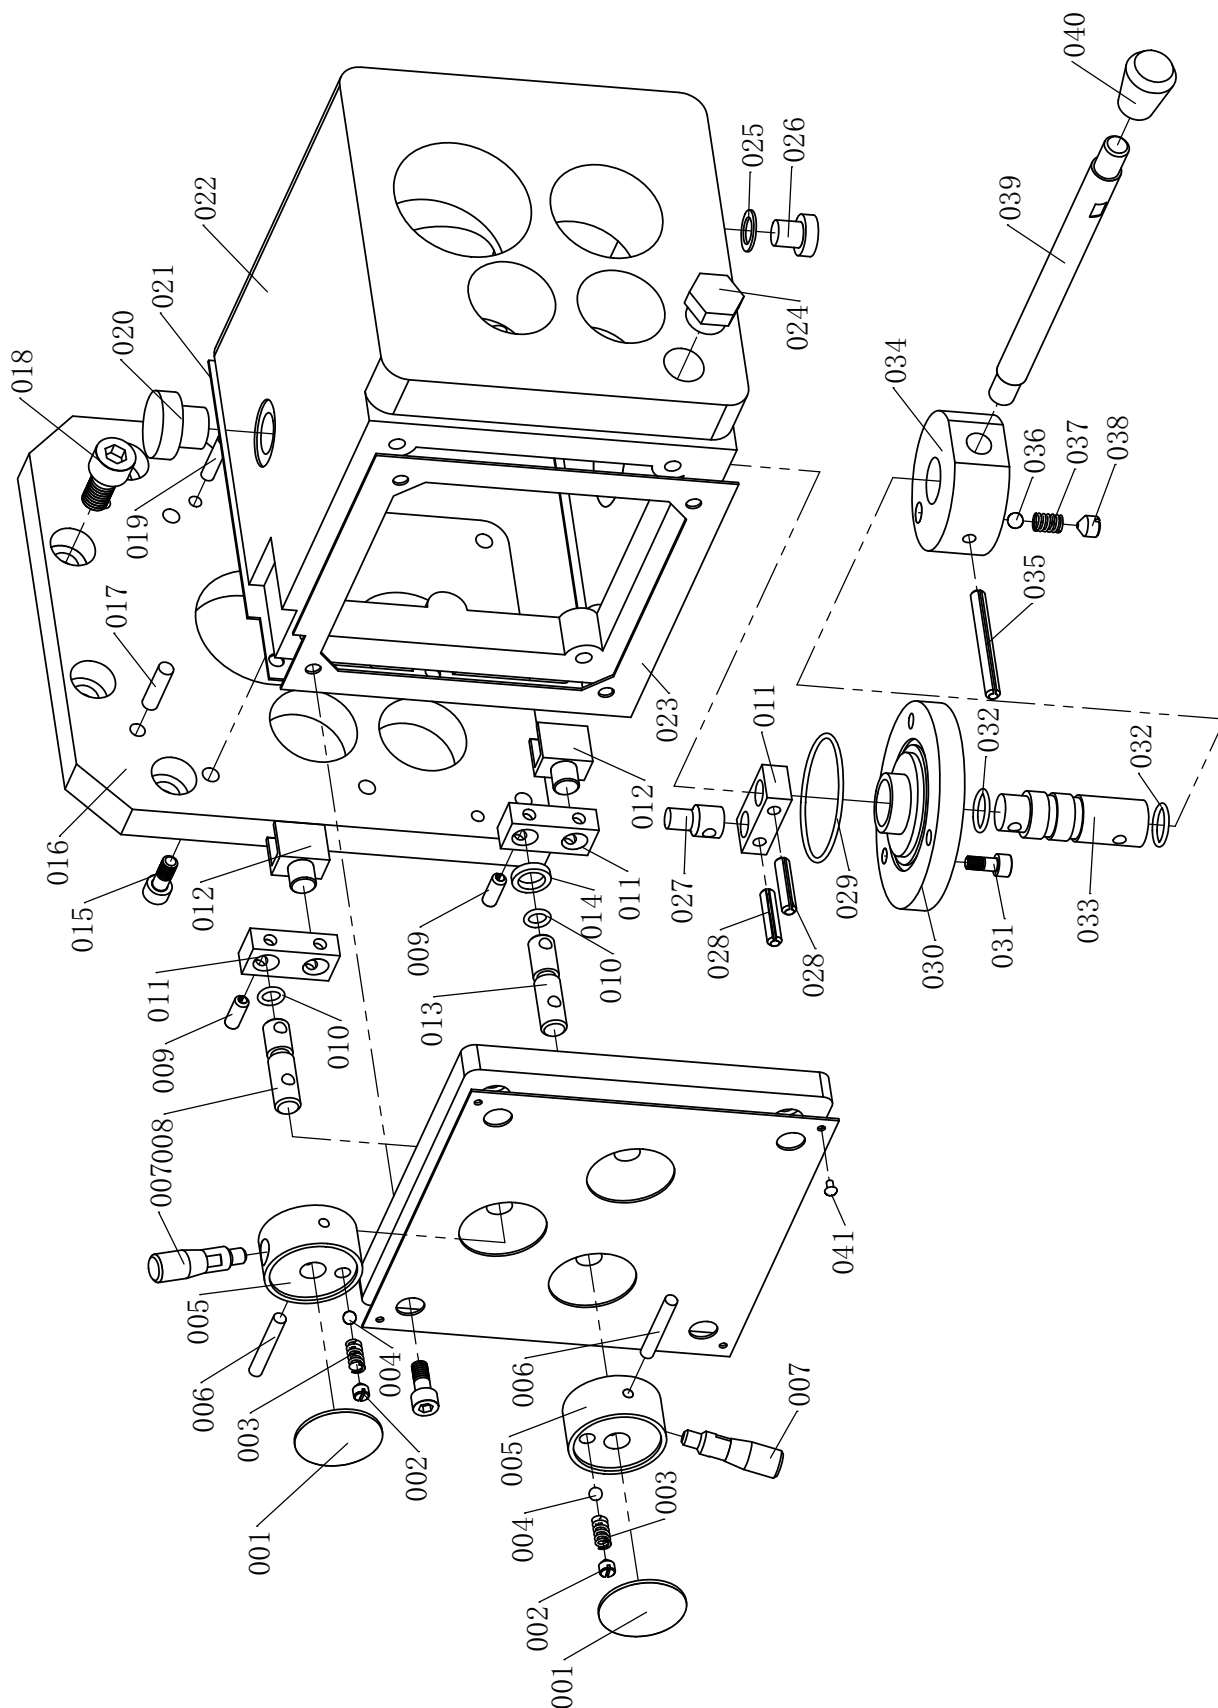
Vorschubgetriebe X-Achse - Feed gear X-Axis 1 - 3
